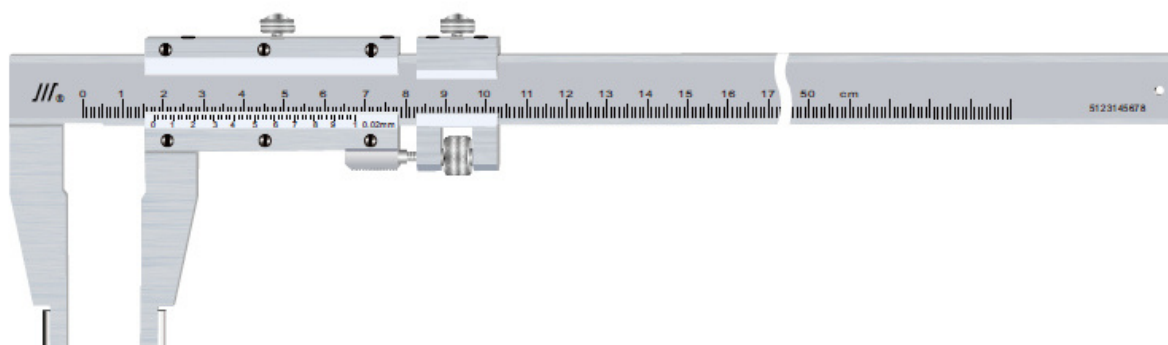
Общий вид штангенциркулей модели ШЦ-III
